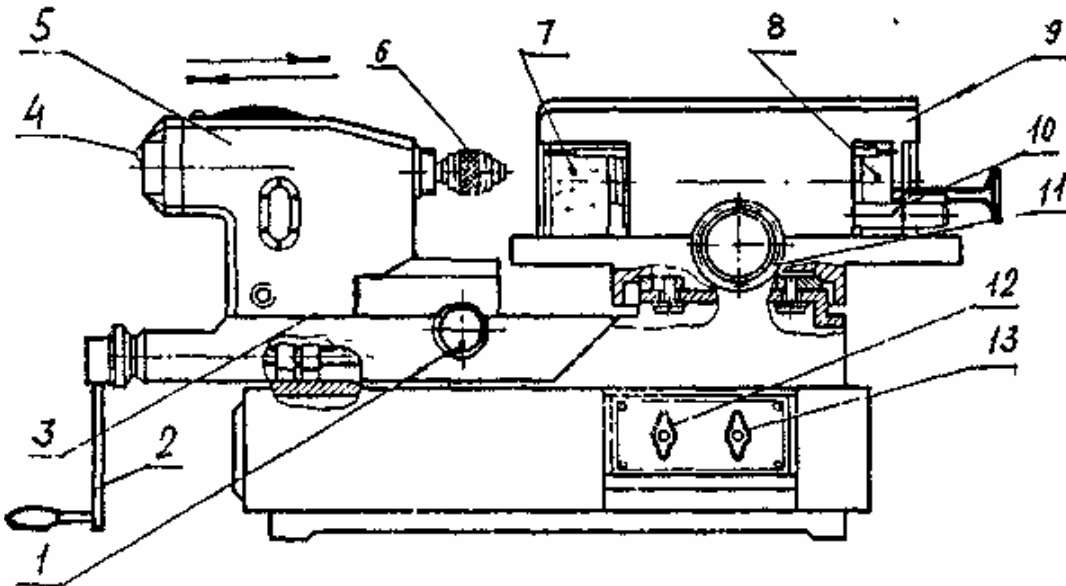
Верстат для шліфування конічної поверхні тарілки і торця стержня клапана.
